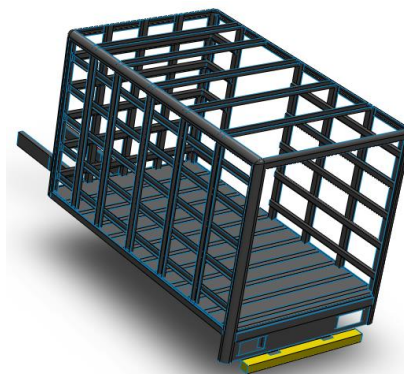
Geometría de la sección posterior del furgón con dispositivo de protección modificado
